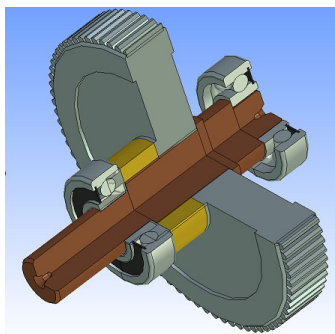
Сборочный чертеж в 3D (параметрическая модель узла)
